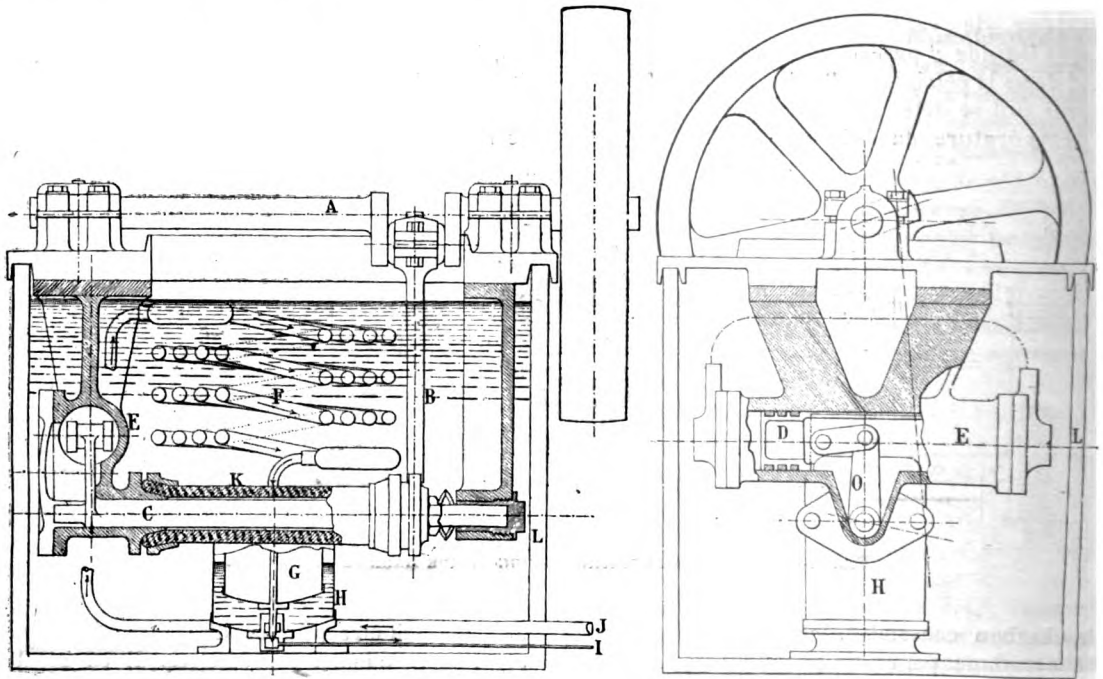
COUPES LONGITUDINALE ET TRANSVERSALE DE LA MACHINE FRIGORIFIQUE MOUGIN ET REPETTO.
